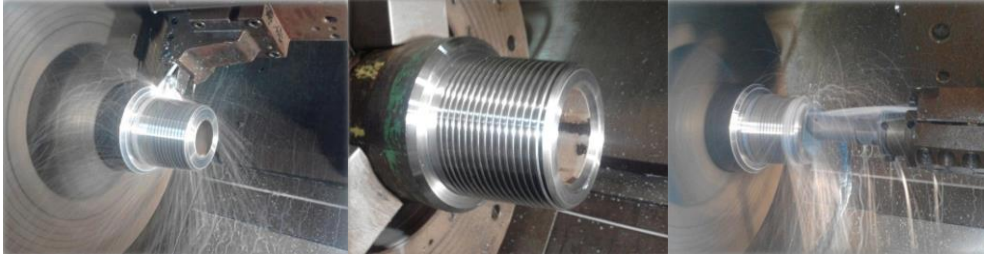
Maquinado de la conexión roscable- piñón a través de torno de CNC
